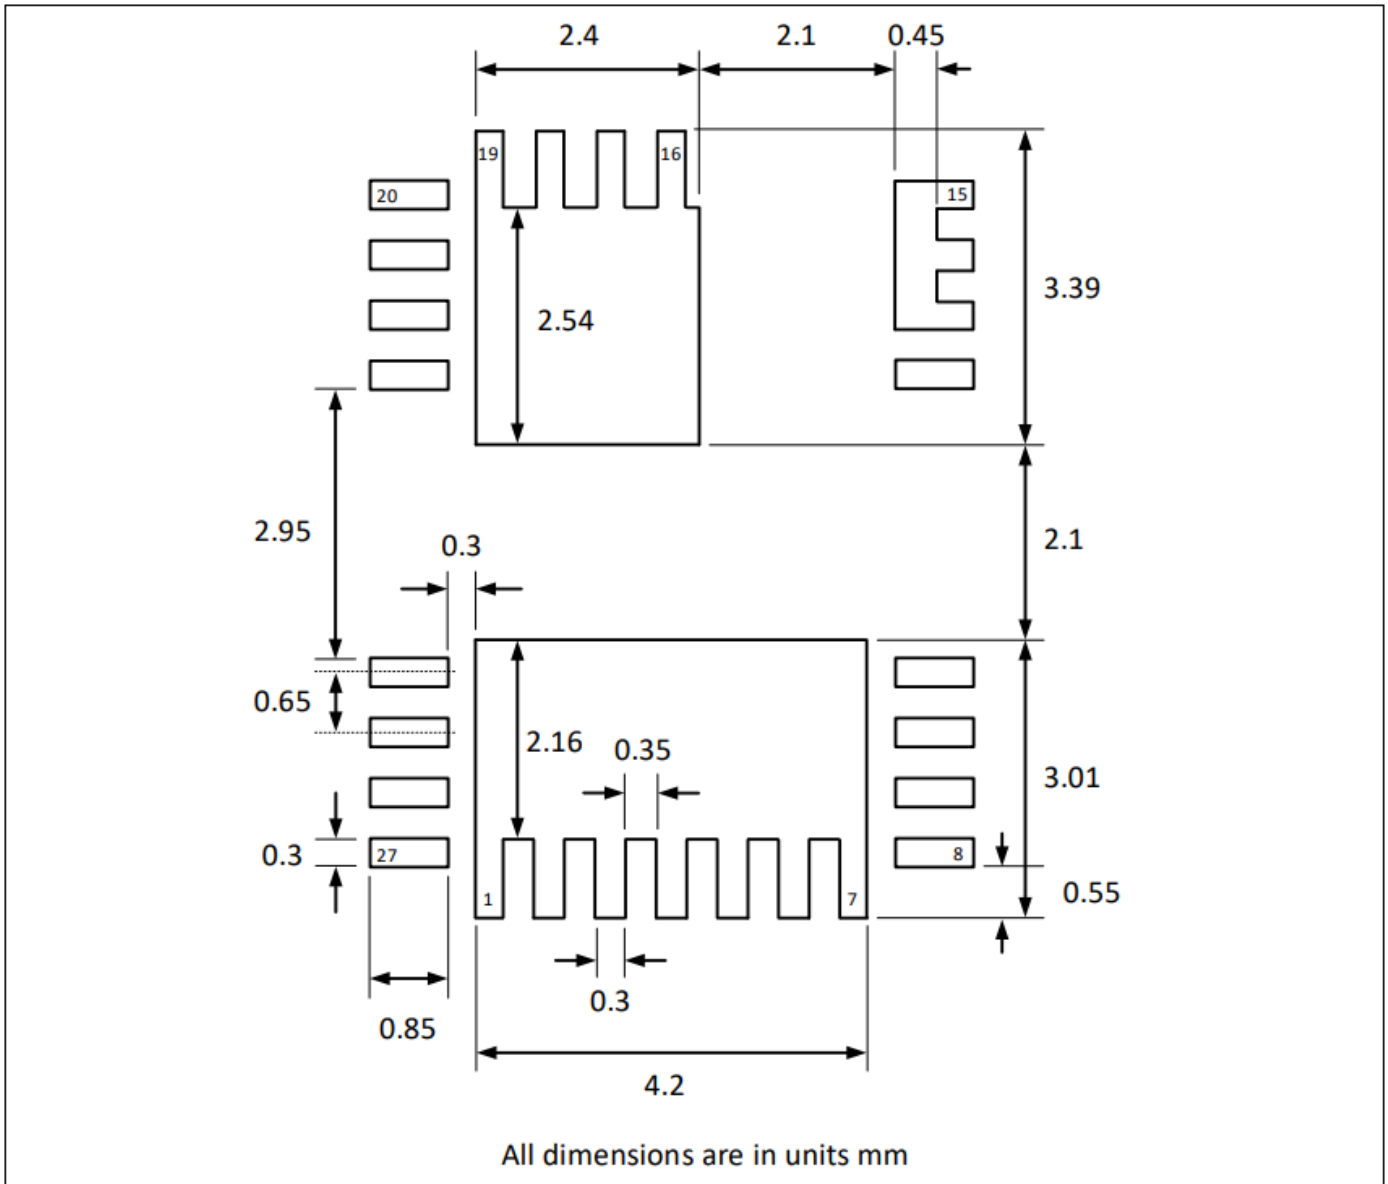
TFLGA-27-2 6x8 PCB 封装尺寸
